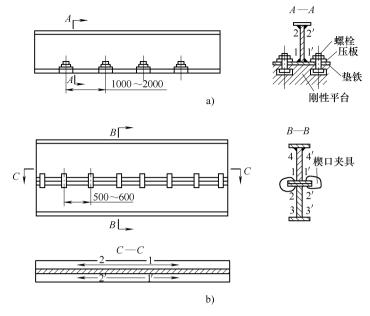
工字梁用刚性夹紧方式进行焊接
